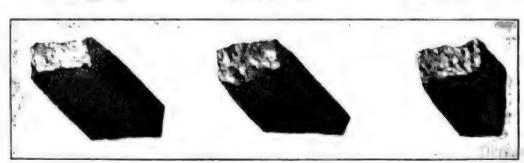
Bruchflächen ber Stäbe. Stab Rr. 4. Stab Rr. 5.
